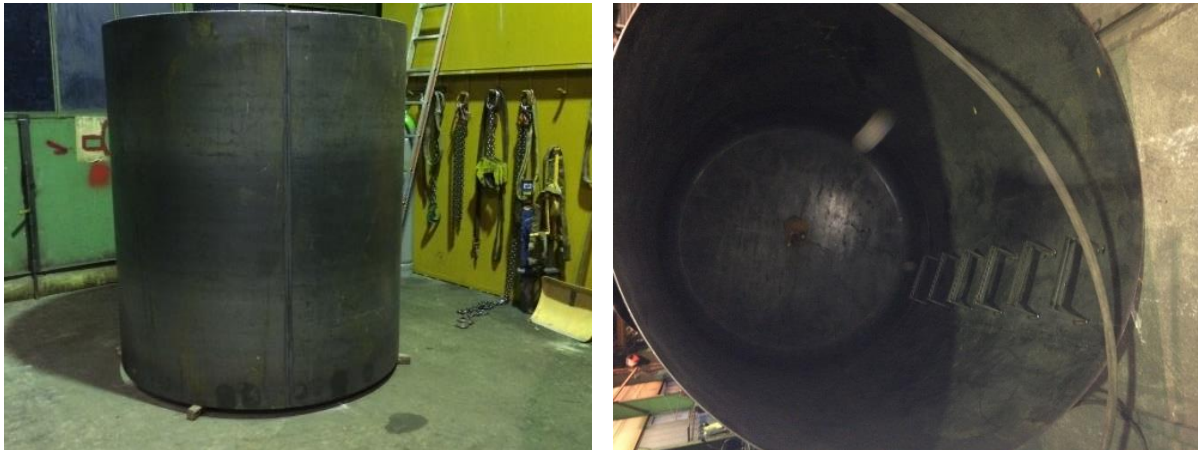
Geschweißter Mantelschuss (links) und Innenspeicher mit Leiterstufen (rechts)
